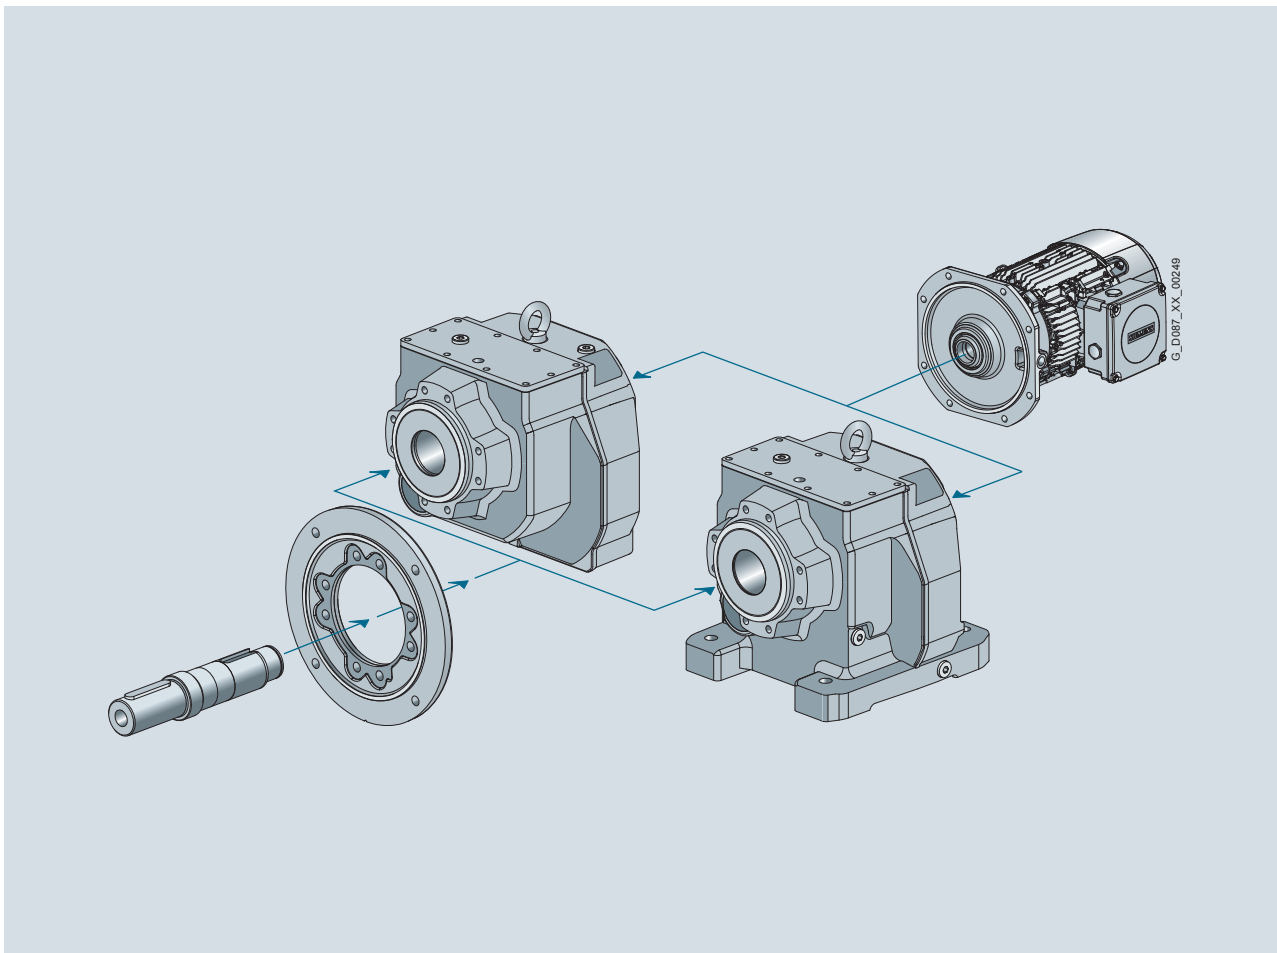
/10 Модуль цилиндрического мотор-редуктора
